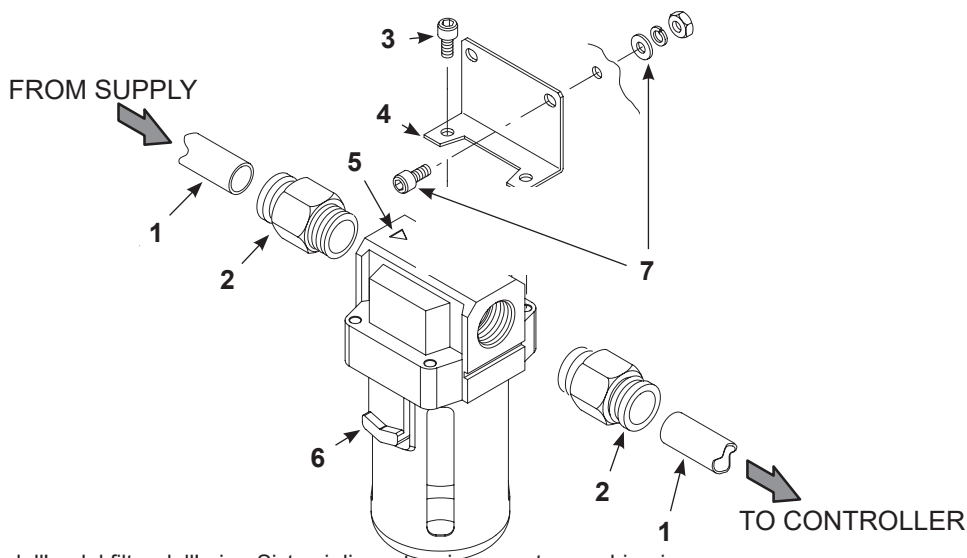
Installazione dell' e del filtro dell'aria - Sistemi di montaggio a parete e su binario
